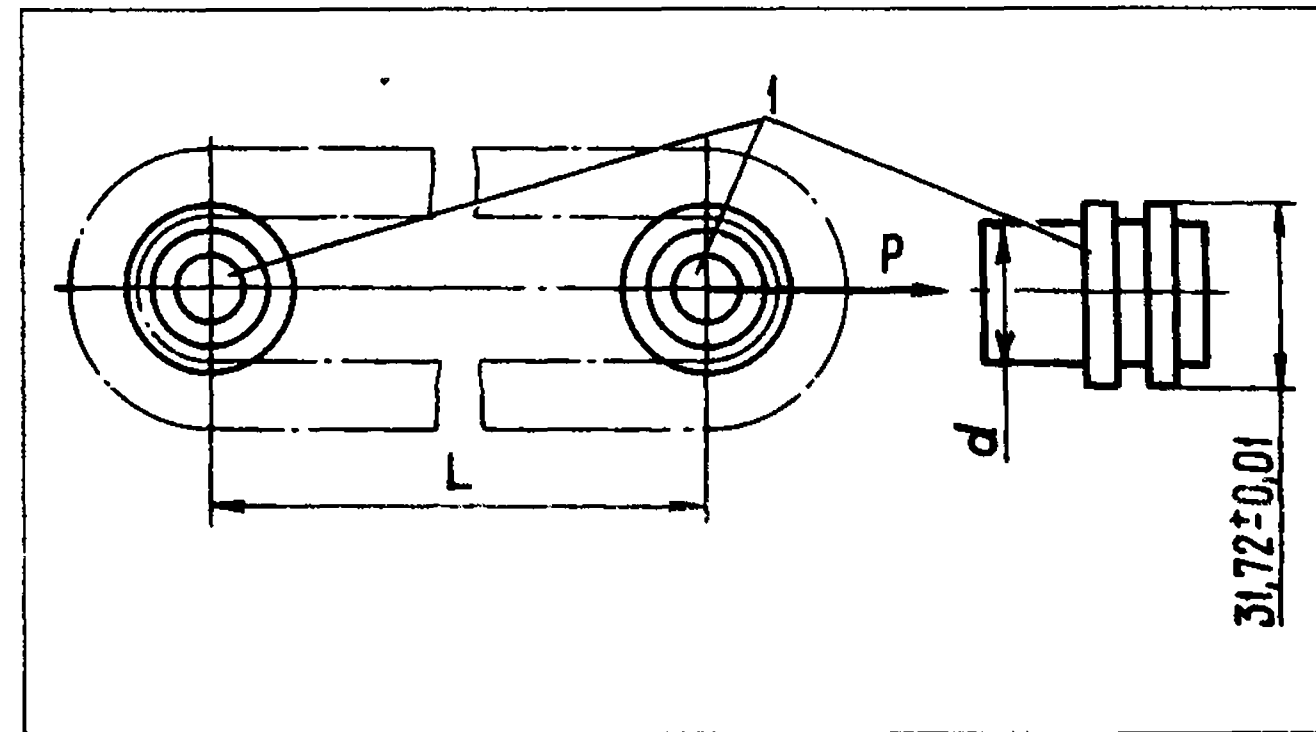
Схема проверки износа (вытяжки) цепи:
